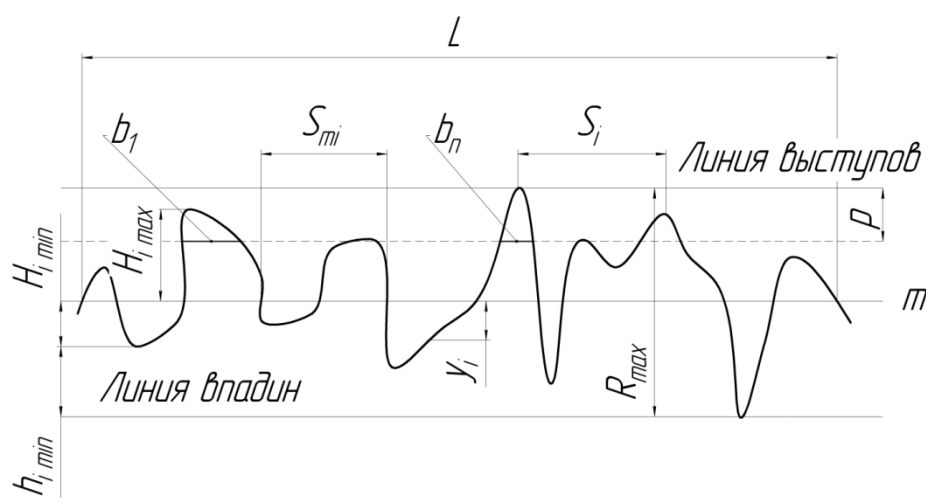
Профиль и параметры шероховатости поверхности
